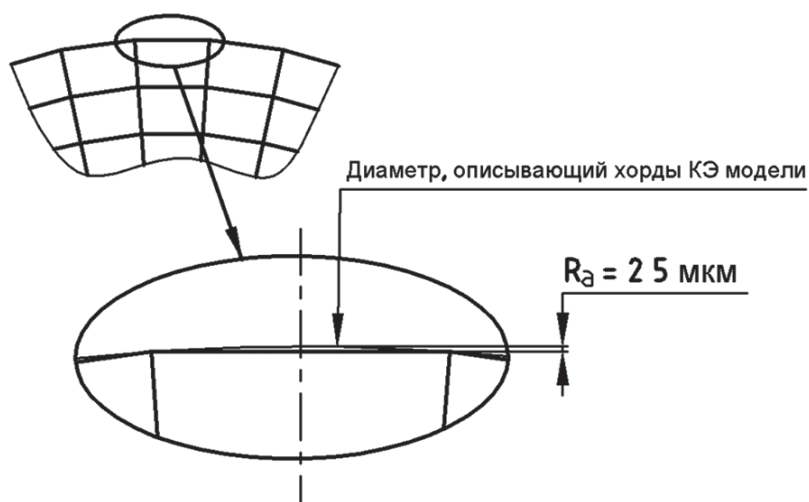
Выбор величины хорды контактных поверхностей подшипника
